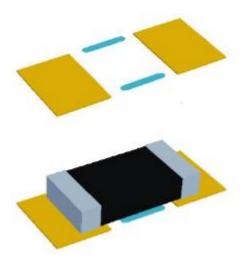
трехмерный вид посадочного места и твердотельная модель ЧИП-резистора
